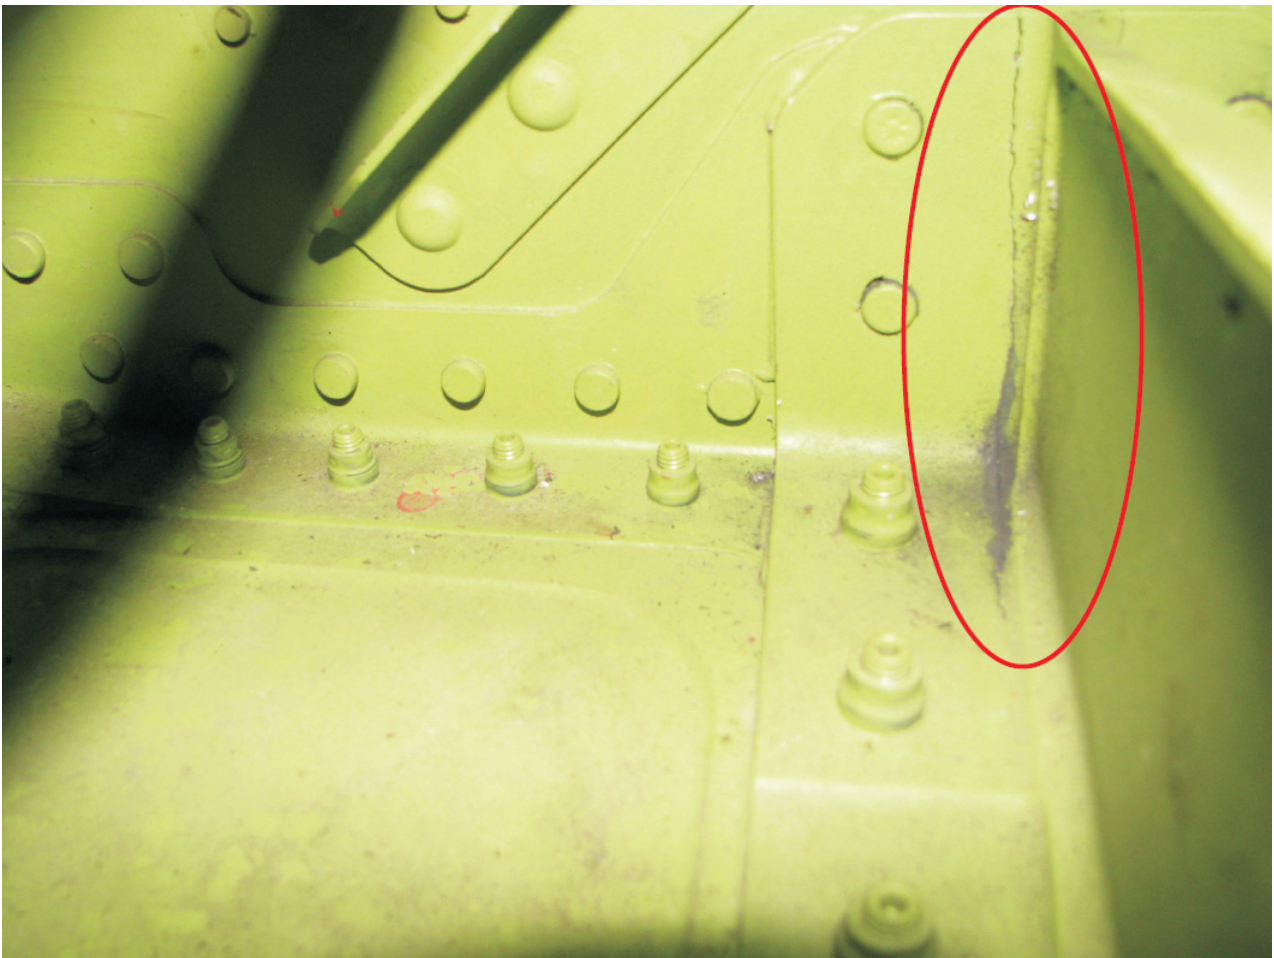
Linke Tragfläche, Anrisse am Flansch des Support Fittings an der Verbindung zu Rippe 7
